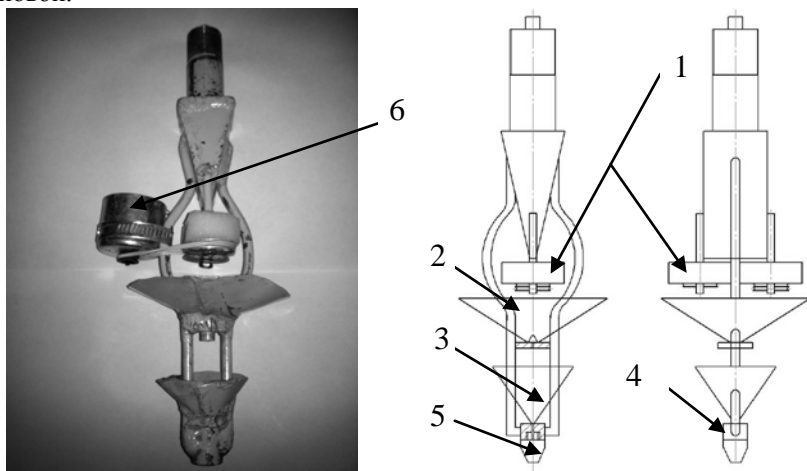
Экспериментальный образец и сборочный чертёж наплавочной головки по предложенному способу:
